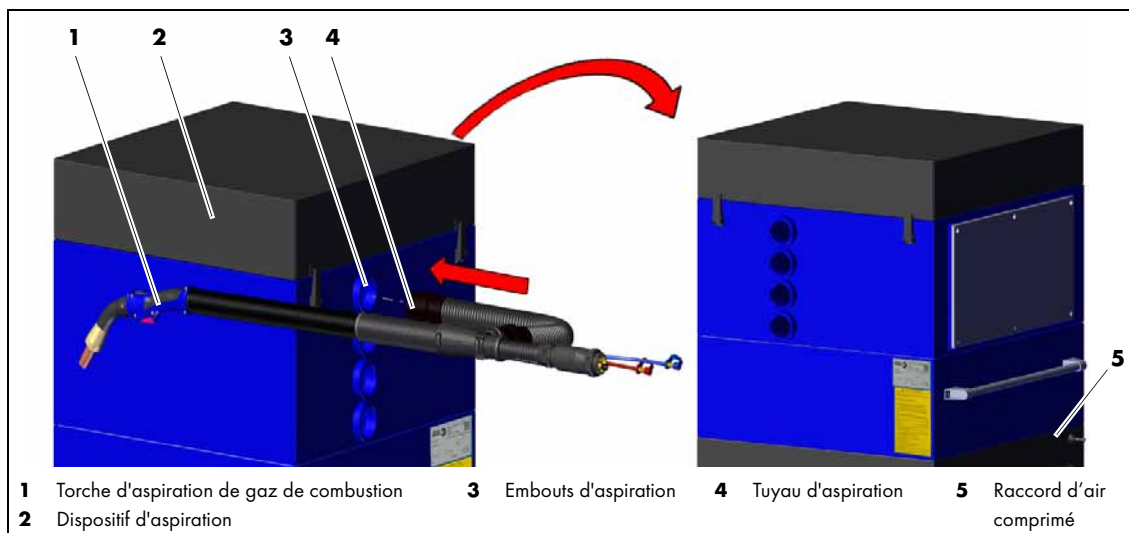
Installation du tuyau d'aspiration de la torche de soudage
